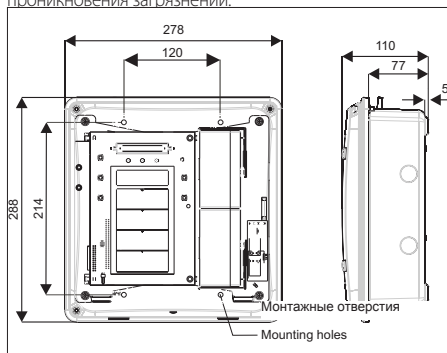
Габаритные размеры Gasmaster и монтажные отверстия
